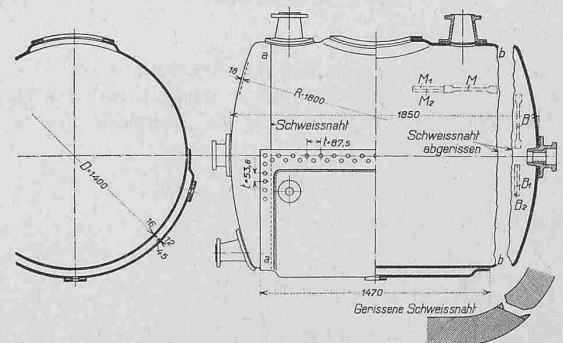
Explodiertes Dampfgefäss. — Masstab 1 : 40. Mit Angabe der Materialproben-Entnahmestellen.
